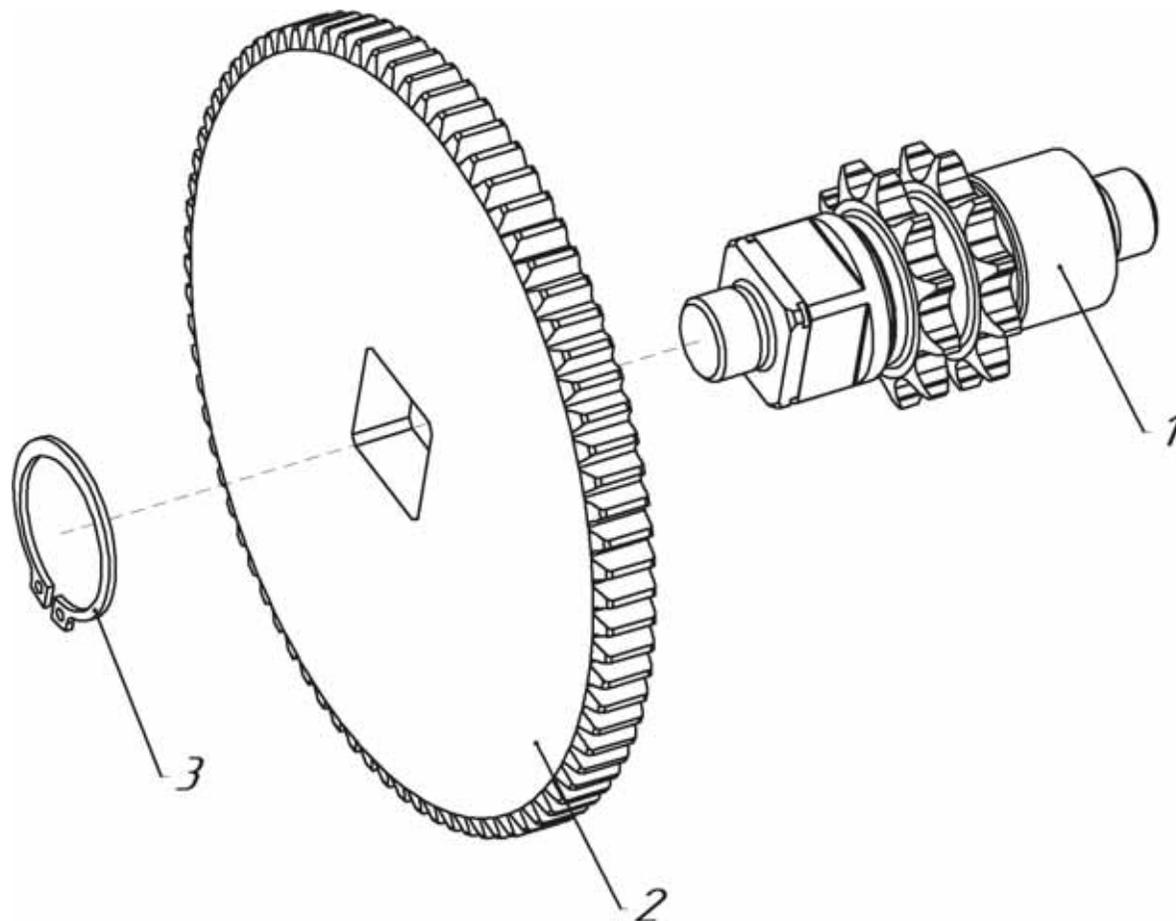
(005.67.0880-01 Вал-звездочка в сборе)
